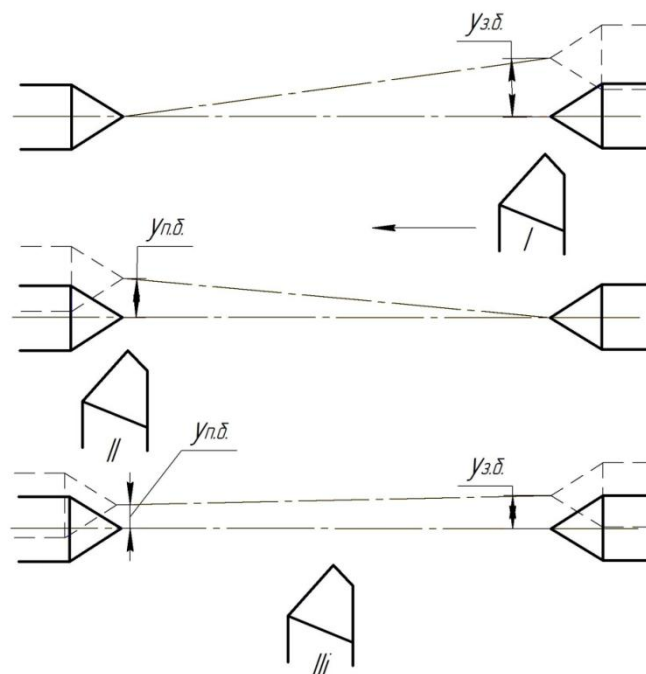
Изменение положения линии центров токарного станка по мере продвижения резца вдоль заготовки при обработке в центрах
